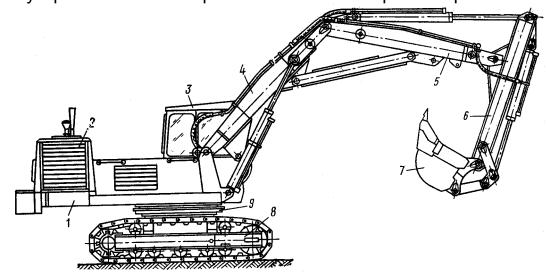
3. Гидравлический экскаватор обратная лопата 1— поворотная платформа; 2— силовая установка; 3— кабина; 4— основная стрела; 5— дополнительная стрела; 6— рукоять; 7— ковш; 8— гусеничная тележка; 9— опорно-поворотное устройство
